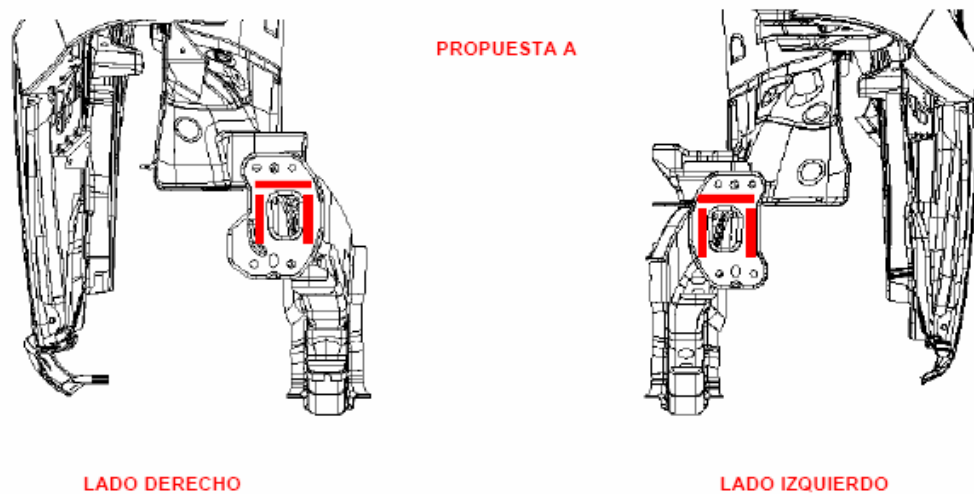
Propuesta A soldadura de tapetas
